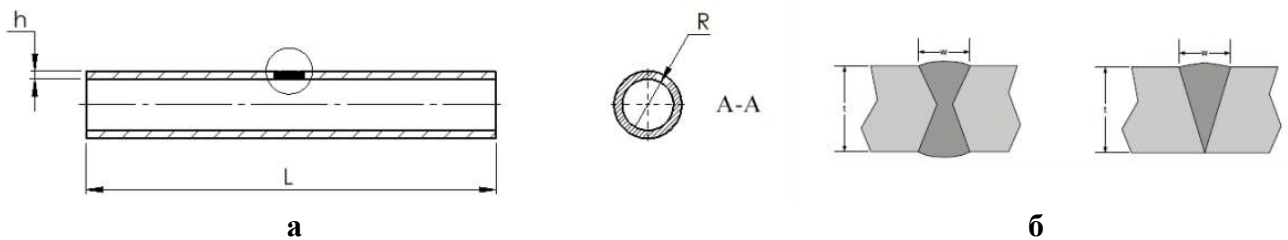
Розрахункова схема задачі: а) геометричні розміри трубопроводу, б) геометричні розміри зварного з'єднання
